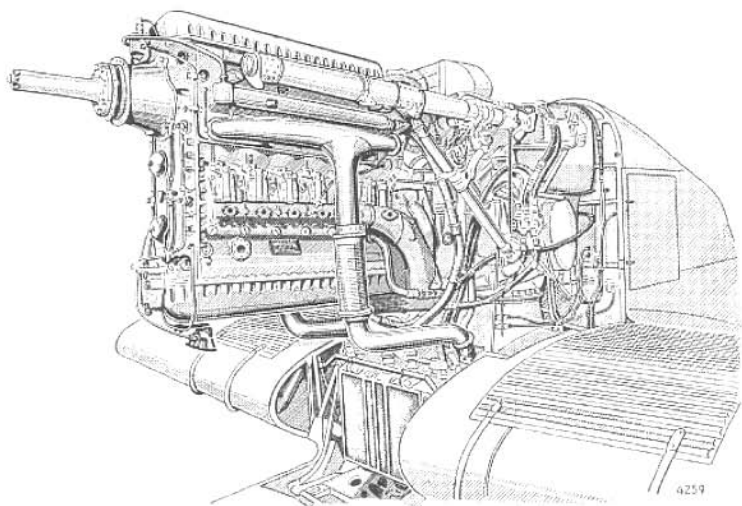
Motoraufhängung JUMO 205 in Ha 138
